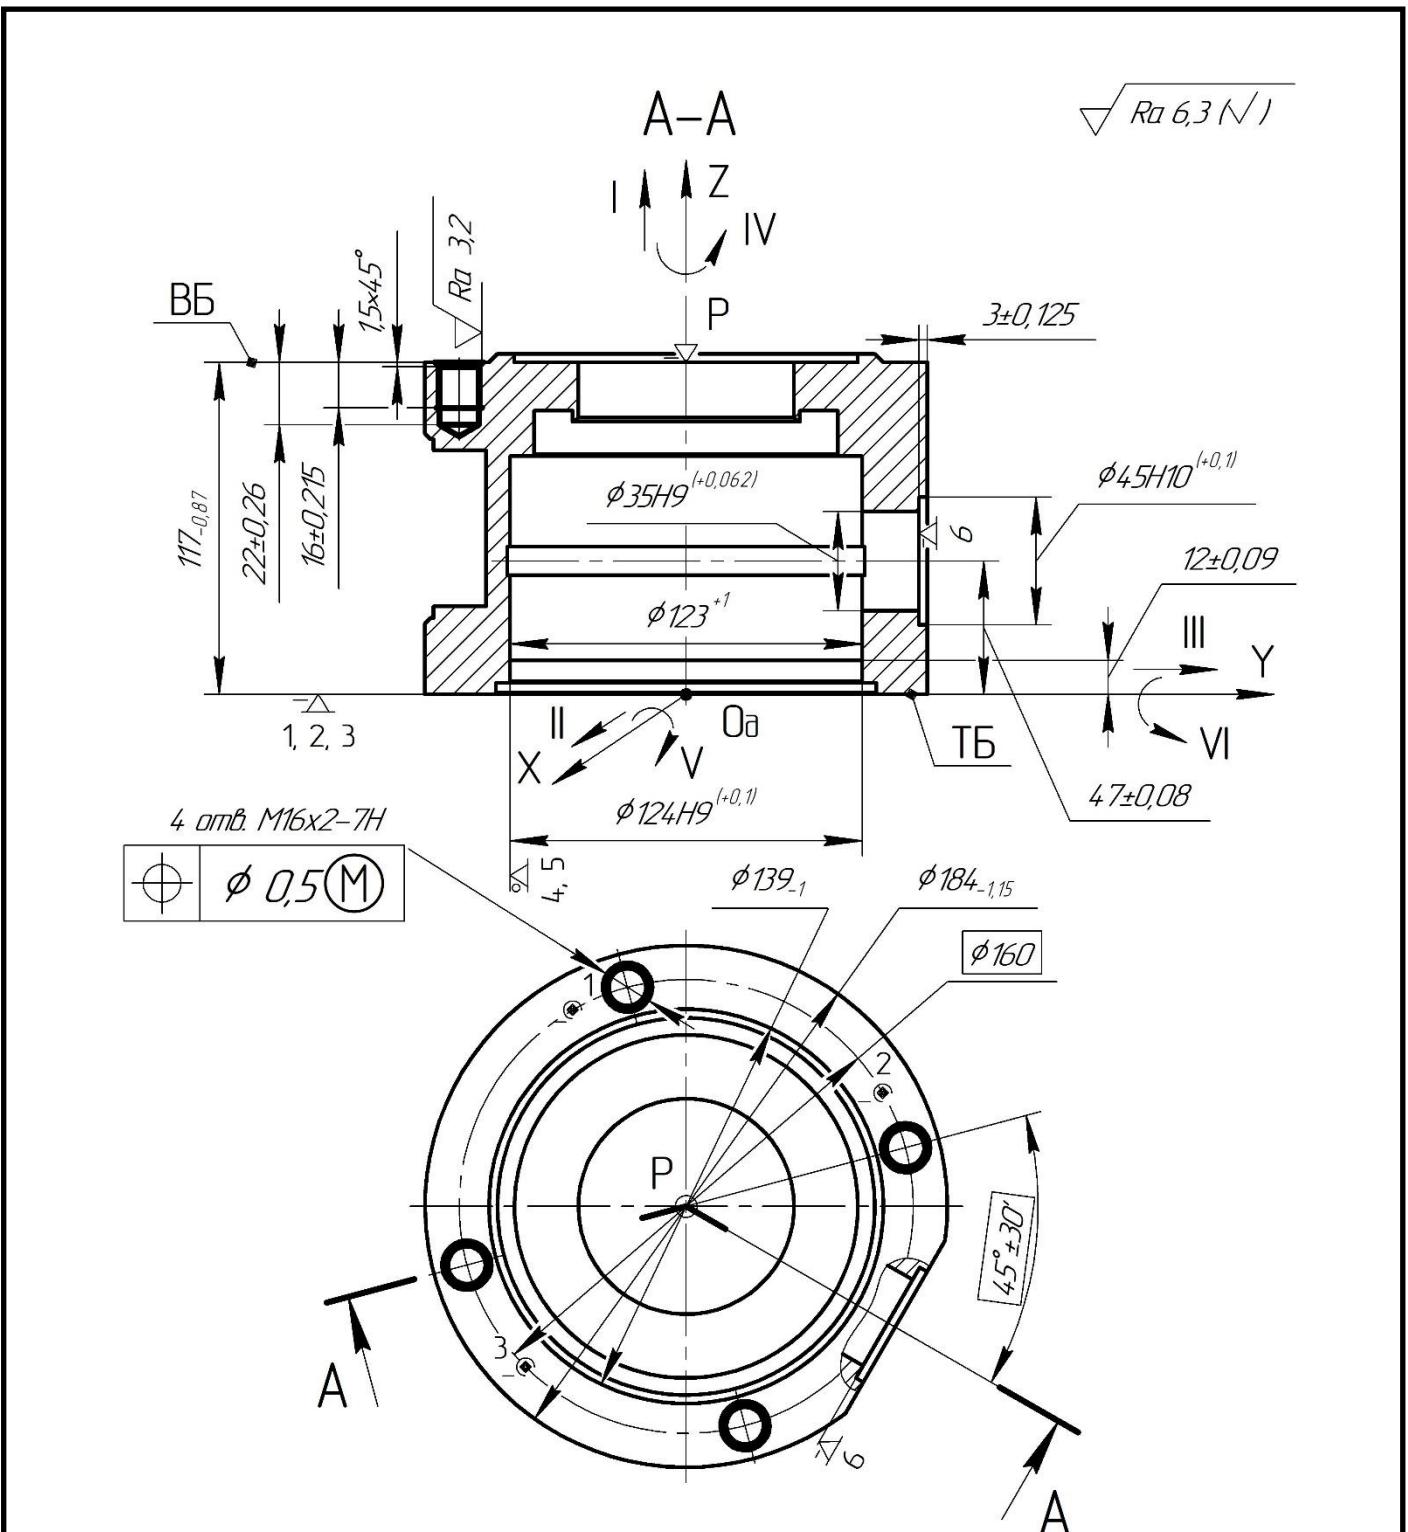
4 – Схема базування заготовки на операції 040 «Свердлильна з ЧПК»
